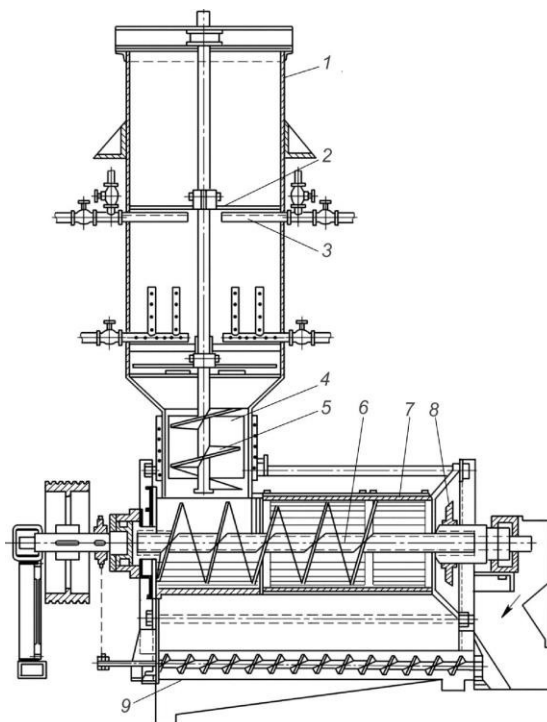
Схема олійного форшнека типу КЯ:
